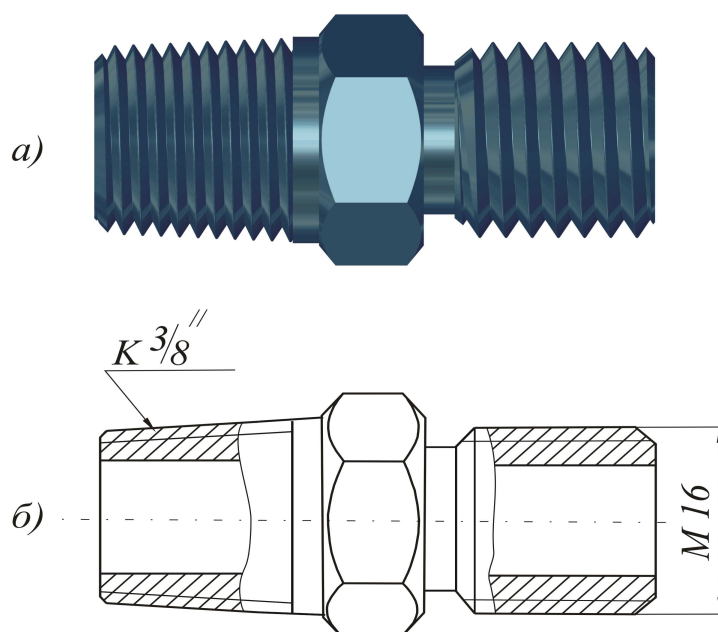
Деталь с конической и цилиндрической резьбой: а) в натуральном виде; б) на эскизе
